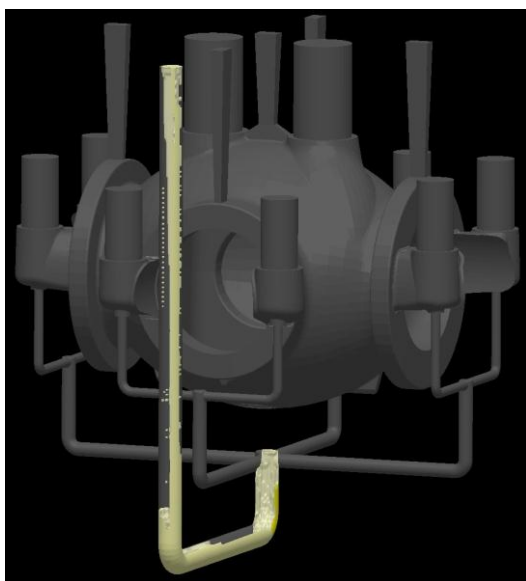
Náhled tvaru geometrie technologie odlitku ve formátu STL uloženého v systému SolidWorks
